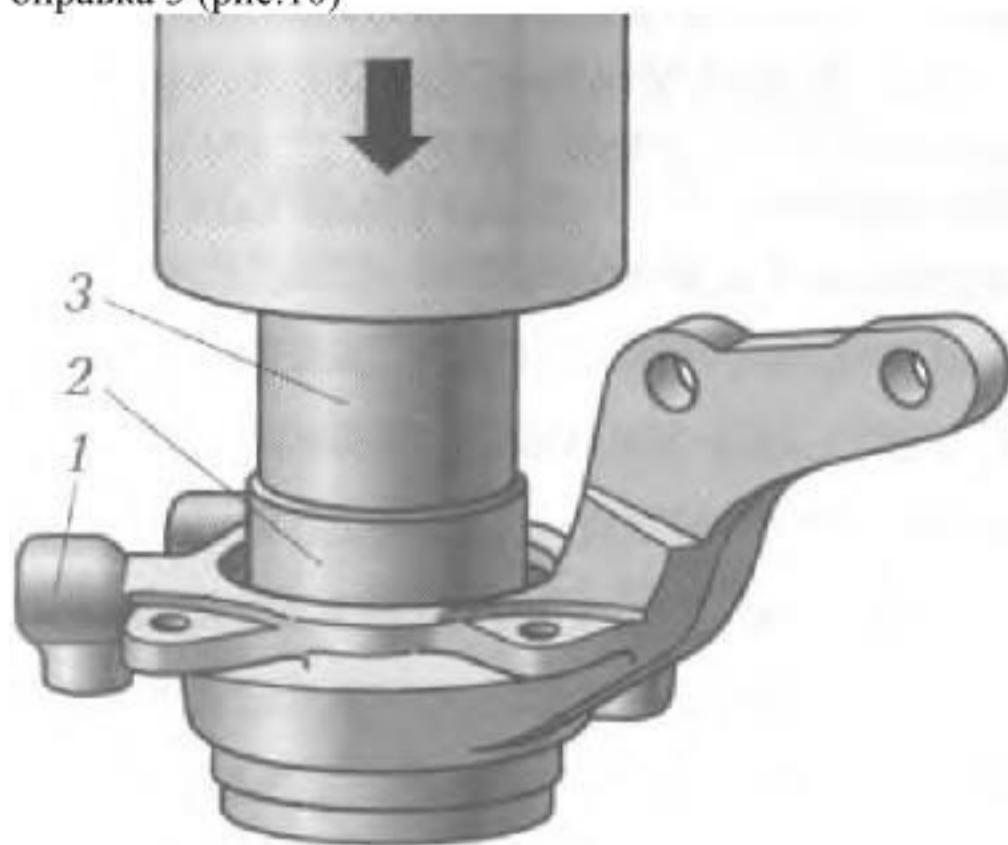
Запрессовка подшипника в поворотный кулак:
